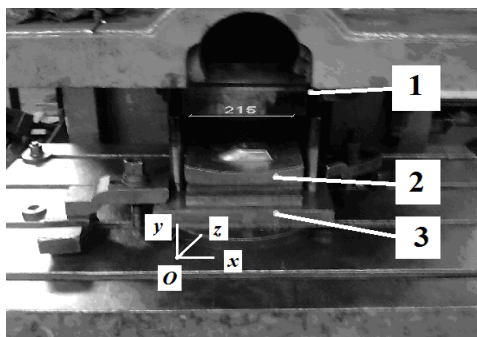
Один из исследуемых штампов, установленный на открытый кривошипный пресс номинальной силой 750 кН:
